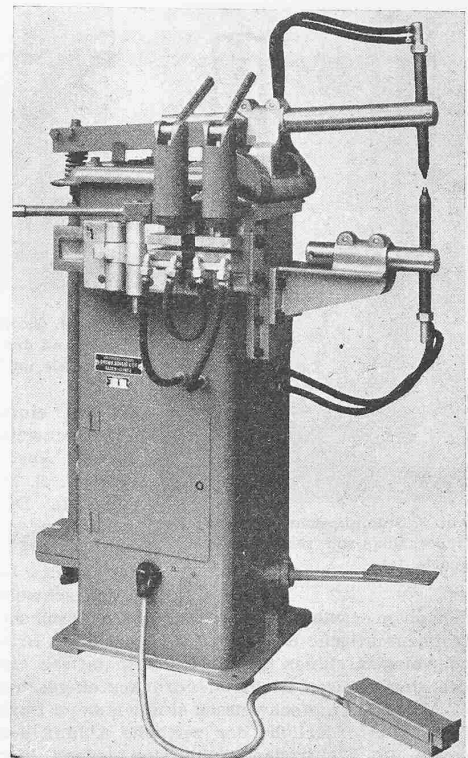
Punktschweissmaschine von 25 kVA Anschlusswert für Stahlblech 2+4 mm mit angebauter Stumpfschweissvorrichtung
